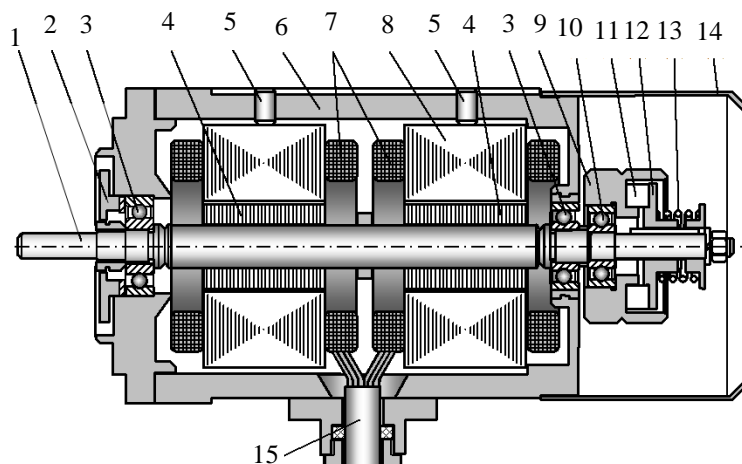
Конструктивний виконавчий пристрій мехатронної системи: 1 – вал ротора; 2 – передній фланець; 3 – підшипник ротора; 4 – пакети магнітопровода ротора; 5 – штифти пакетів магнітопровода; 6 – корпус статора; 7 – обмотки фаз статора; 8 – пакети магнітопровода статора; 9 – інерційний демпфер; 10 – підшипник демпфера; 11 – фрикційна прокладка; 12 – натискна шайба демпфера; 13 – пружина демпфера; 14 – кожух демпфера; 15 – виводи обмоток фаз статора.
